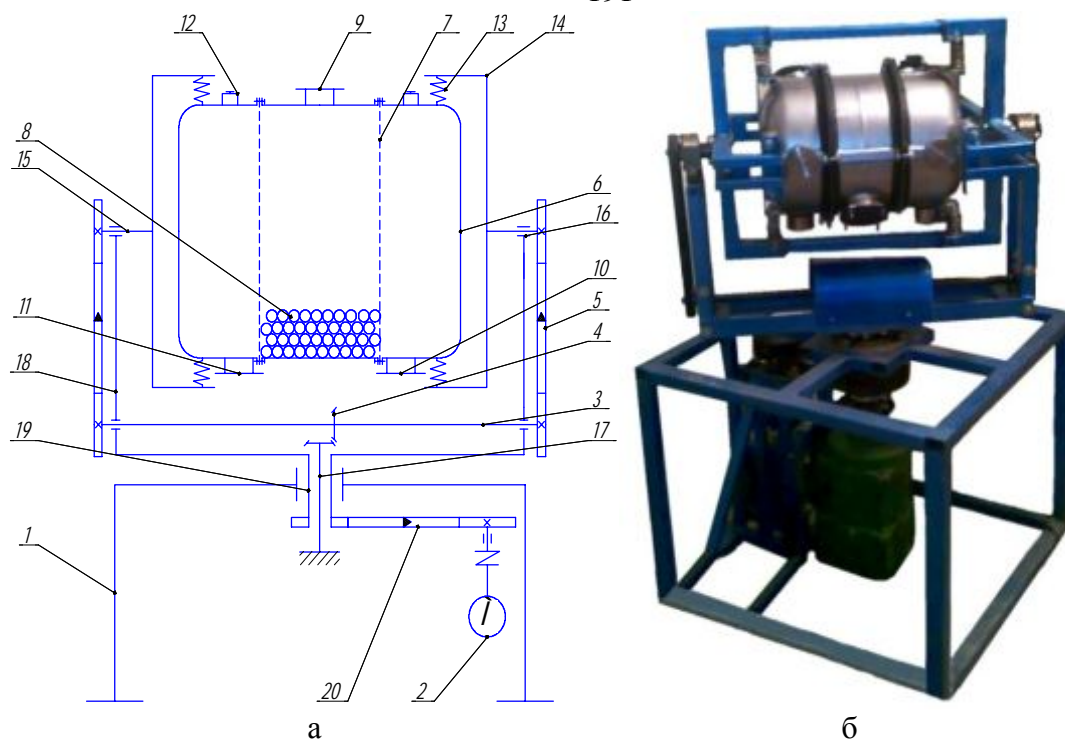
Розроблений вібровідцентровий дезінтегратор: а – принципова схема; б – розроблене обладнання; 1 – станина; 2 – електродвигун; 3, 15, 17, 19 – приводні вали; 4 – конічна передача; 5, 19 – клинопасові передачі; 6 – трикамерний контейнер; 7 – ситові елементи; 8, 9, 10 – патрубки; 11 – незрівноважені маси; 12 – пружні елементи; 13 – обод; 15 – підшипникові вузли; 16 – проміжний вал; 17 – водило.
